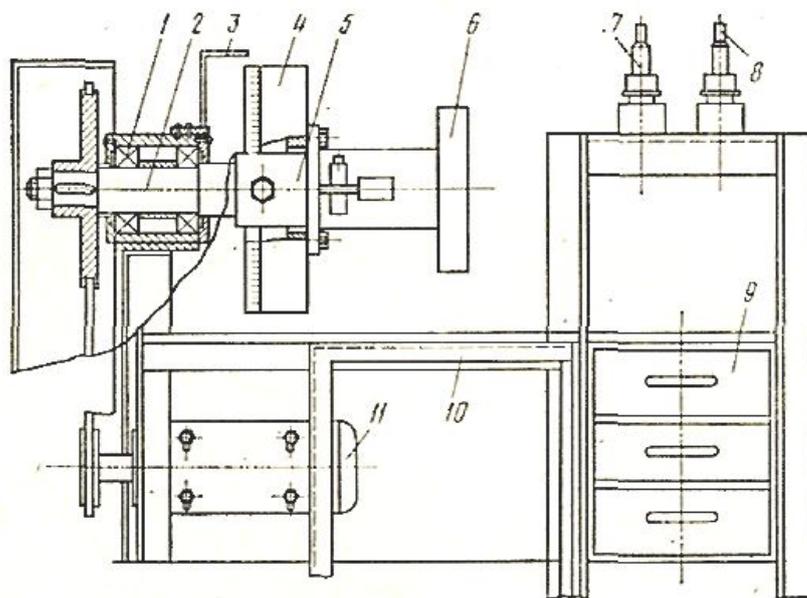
Стенд для обкатки и регулировки приемных коробок ткацкого станка СТБ.
